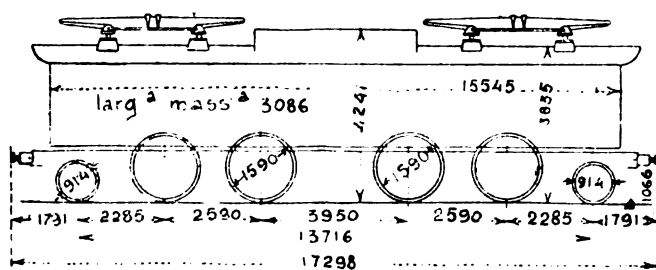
Schema e dimensioni principali del locomotore per treni passeggeri.
